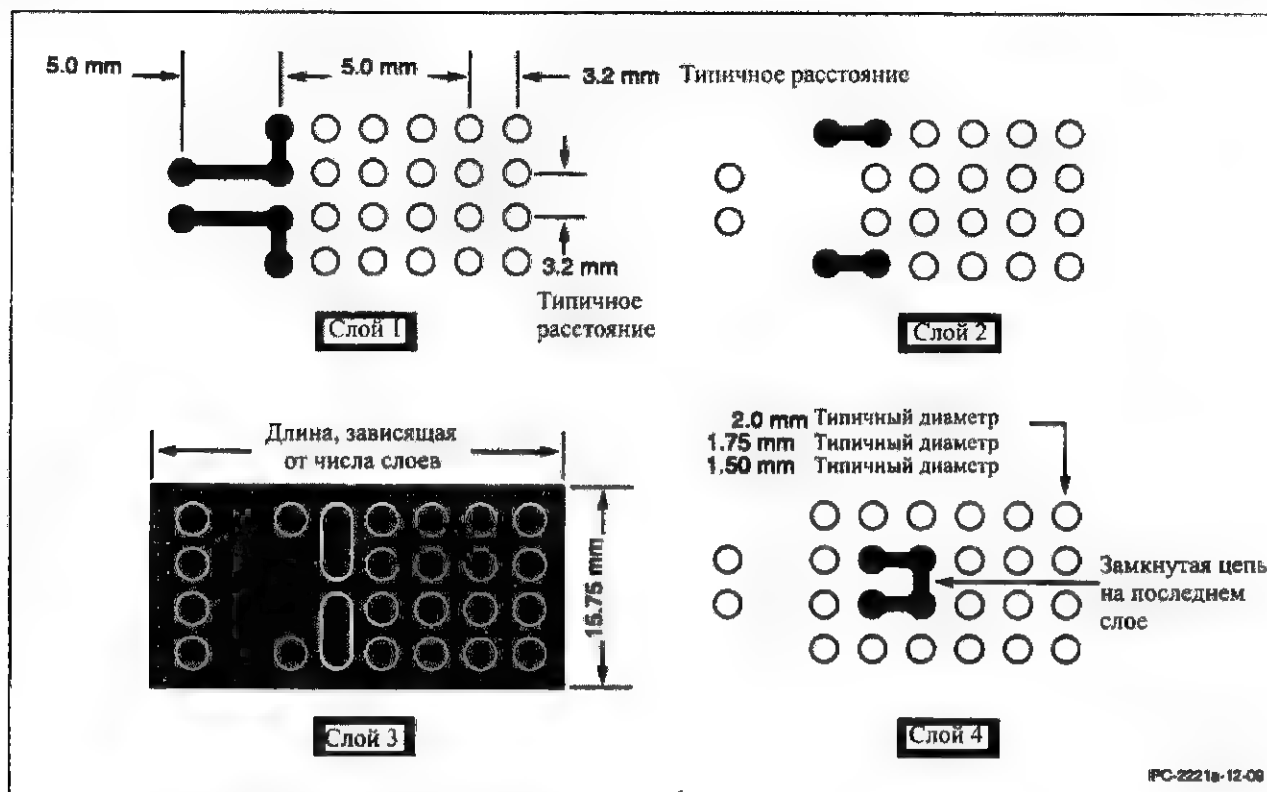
Купон D для контроля процесса изготовления 4^х слойной платы
